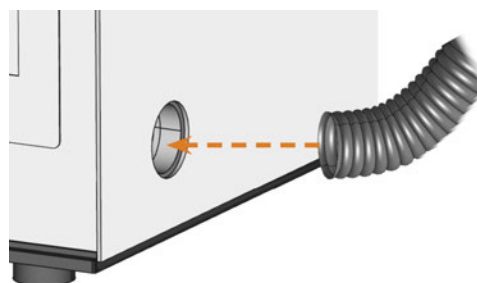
INSÉRER LE TUYAU D'ASPIRATION DANS LA MACHINE
